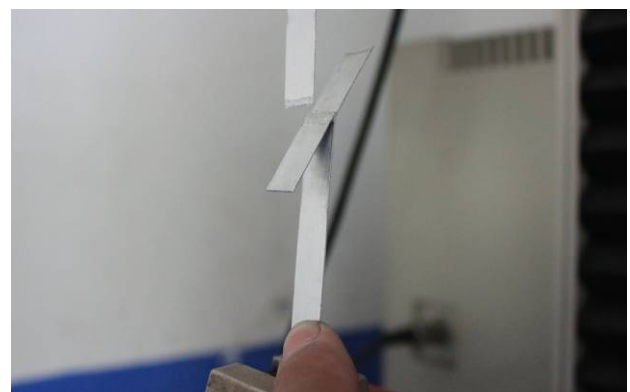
Hasil proses FSW *Lap welding*, tampak atas
